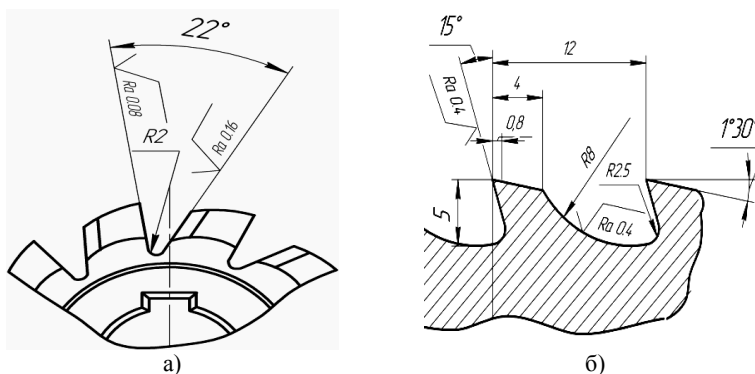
Профиль стружечных канавок: а – червячной фрезы; б – протяжки
